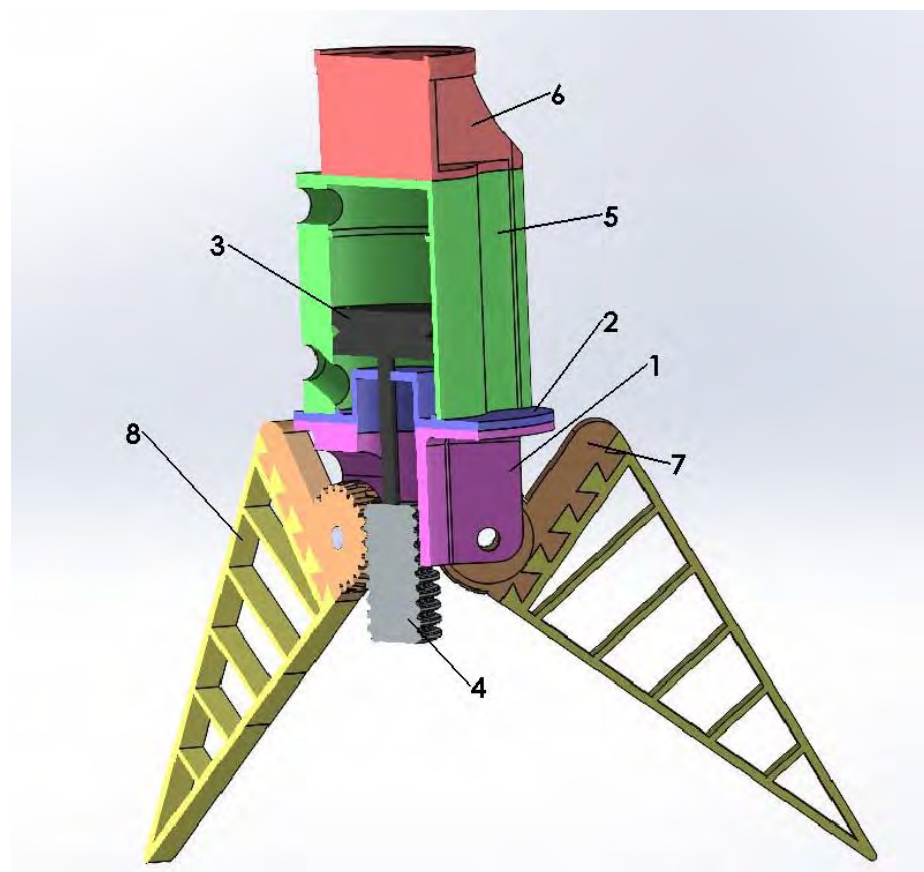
Вид в розрізі моделі м'якого захвату. 1 - основа хвату; 2 - кріплення низу; 3 – поршень; 4 – черв'як; 5 – циліндр; 6 - кріплення до робота; 7 – тверда частина захвату; 8 – м'яка частина захвату.
